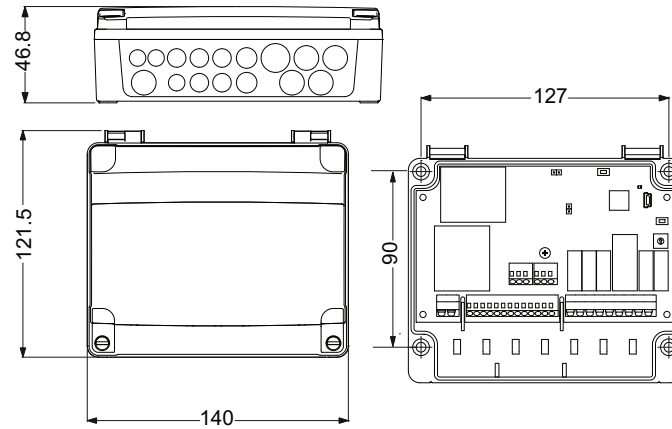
Dimensioni (mm) unità AHS2-0MM.
